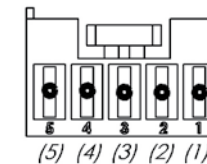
CONNETTORE MOTORE VISTA LATO DI INGRESSO DEI FILI
